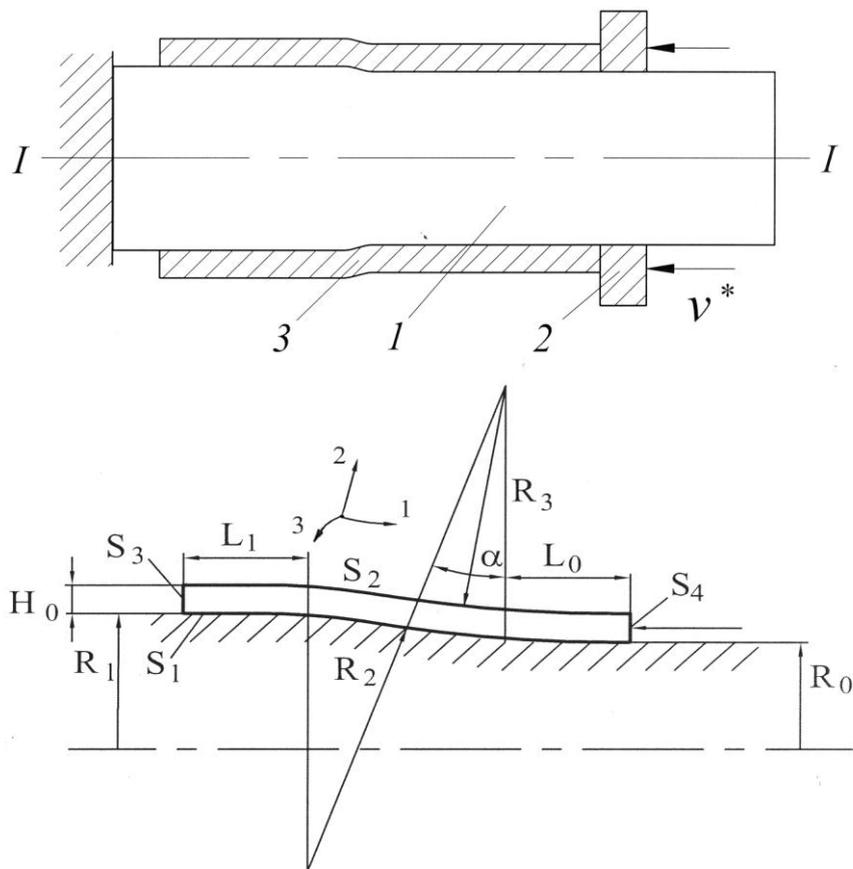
Схема калибровки раздачей трубной заготовки по жесткому пуансону: *1* – пуансон; *2* – упорное кольцо; *3* – трубчатая заготовка
